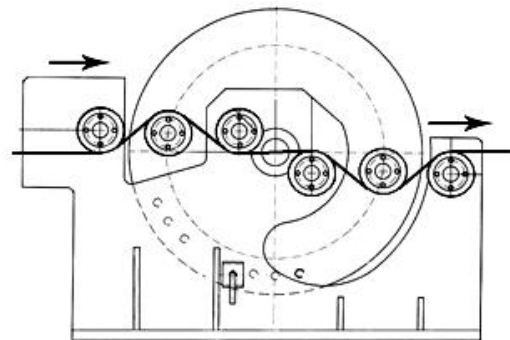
Схема конструкции устройства (окалиноломателя) знакопеременного изгиба калиброванного проката (стрелками указано направление передвижения проката) / Fig. 2. Scheme of the construction of the device (mechanical descaling machine) of the alternating bending of the calibrated rolled steel (the arrows indicate the direction of rolling movement)
